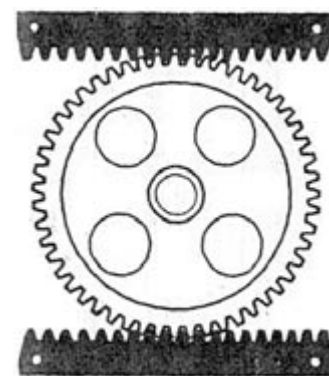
Схема реечного привода эскалатора фирмы «РНВ»
